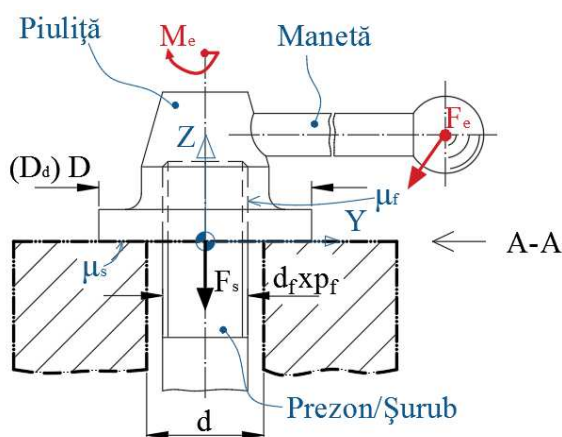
Mecanism de fixare cu piuliță cu guler plat – prezentare schematică
